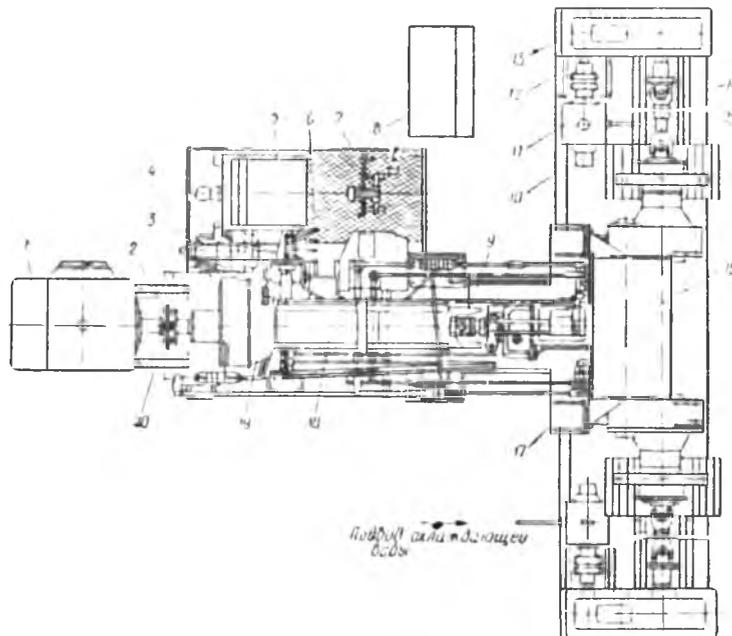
Стенд ОИ-55 для обкатки и регулировки блока силовой передачи трактора ТТ-4:
